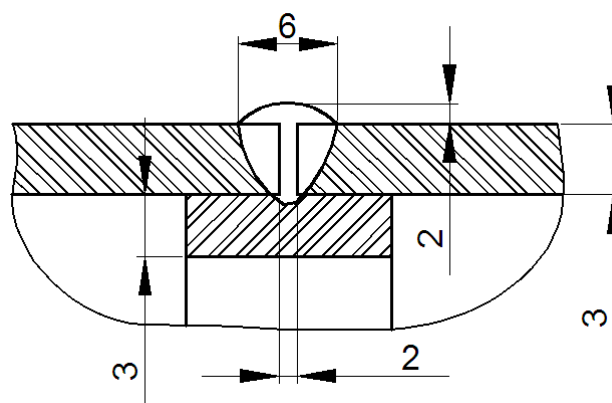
Схема зварного стикового з'єднання С2 за ГОСТ 8713-79
